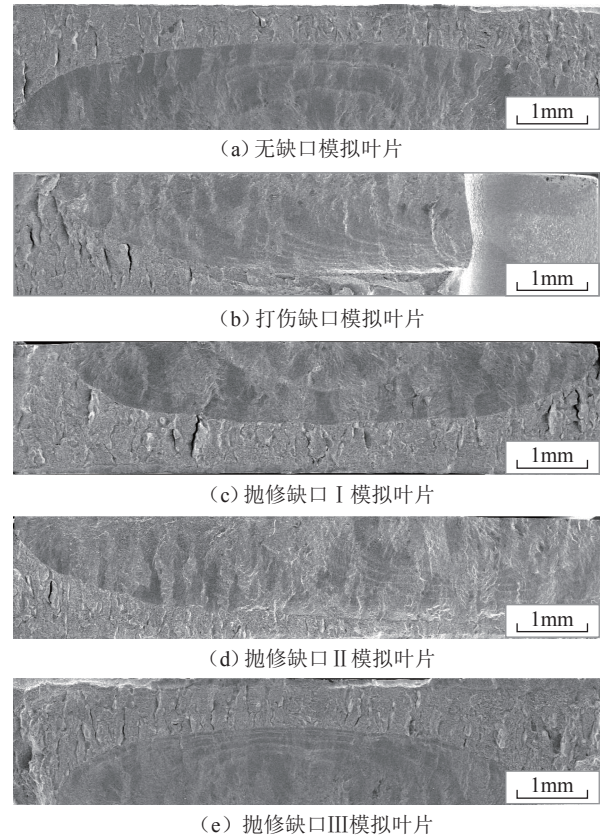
模拟叶片疲劳断口在扫描电镜中的低倍放大形貌
